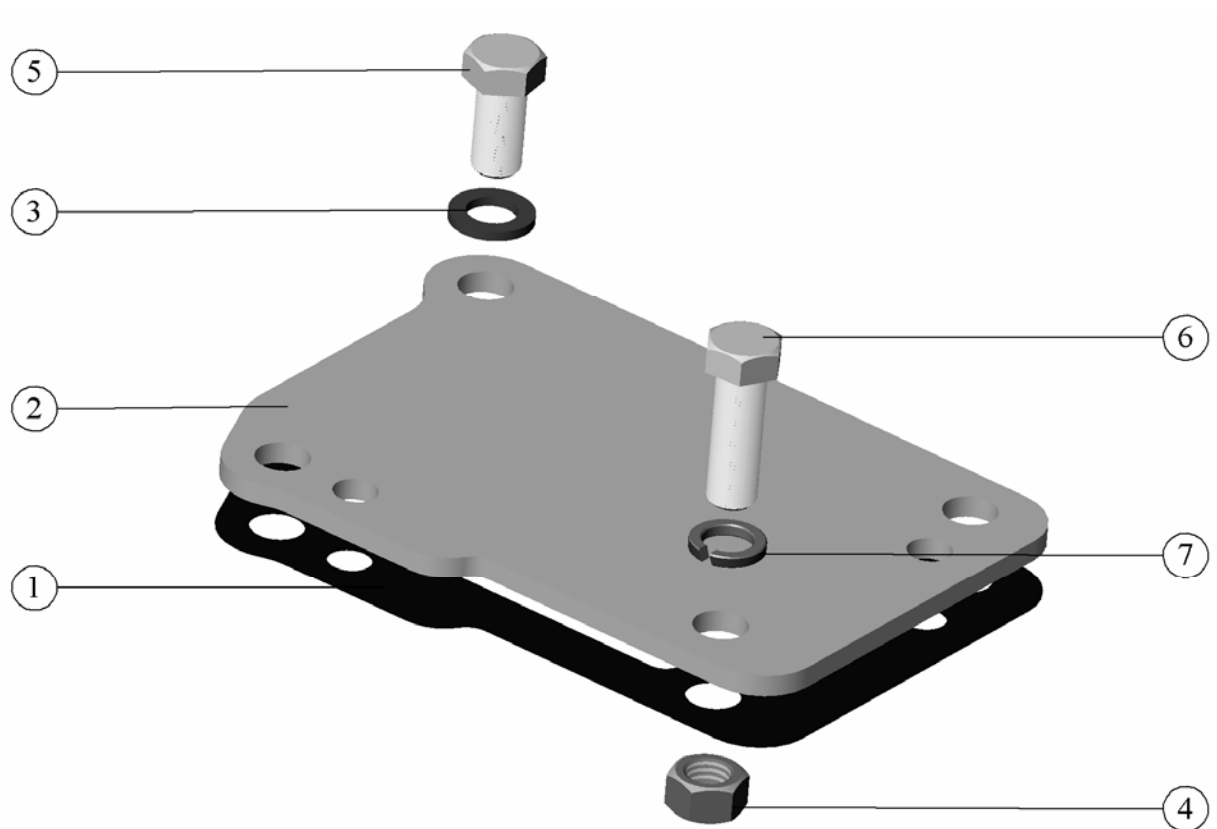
Установка заглушки (для тракторов без пневмокомпрессора)
